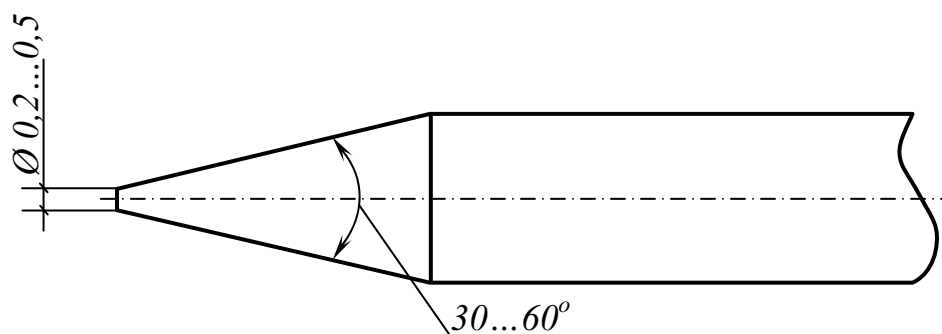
Подготовка вольфрамового электрода перед сваркой
